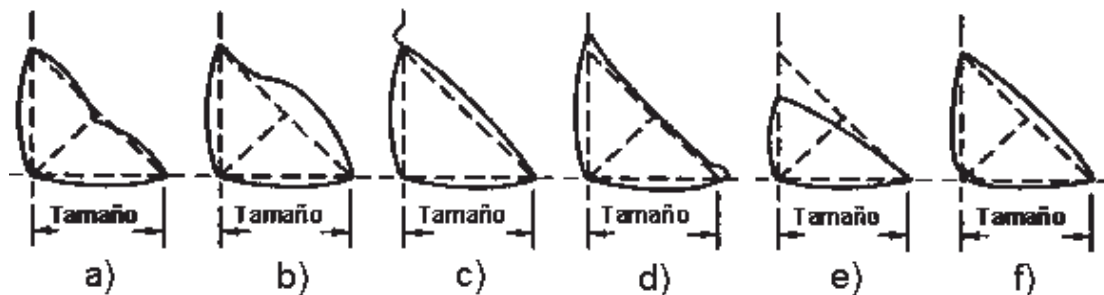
Defectos típicos en soldaduras de filete, a) Garganta insuficiente, b) Convexidad excesiva, c) Socavado excesivo, d) Solapes, e) Lado insuficiente y f) Fusión incompleta.
